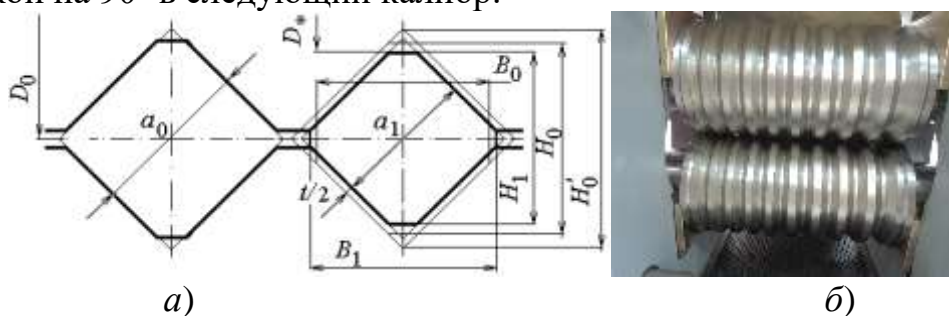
Схема прокатки по системе калибров квадрат-квадрат(а) и вид калибровки валков для прокатки квадратных профилей стана фирмы «Mario Di Maio» (б)
